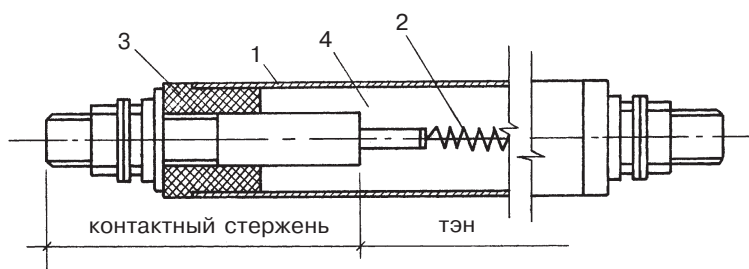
Устройство трубчатого электронагревателя (тэна): 1 — металлическая оболочка; 2 — спираль; 3 — изолятор; 4 — периклаз
